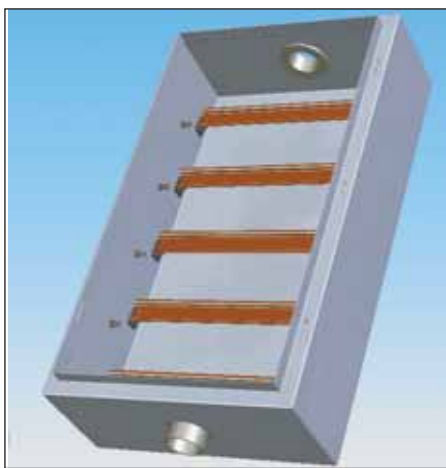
Корпус в исполнении для модульной конструкции с установленными стыковочными втулками и рейками для крепления аппаратов
